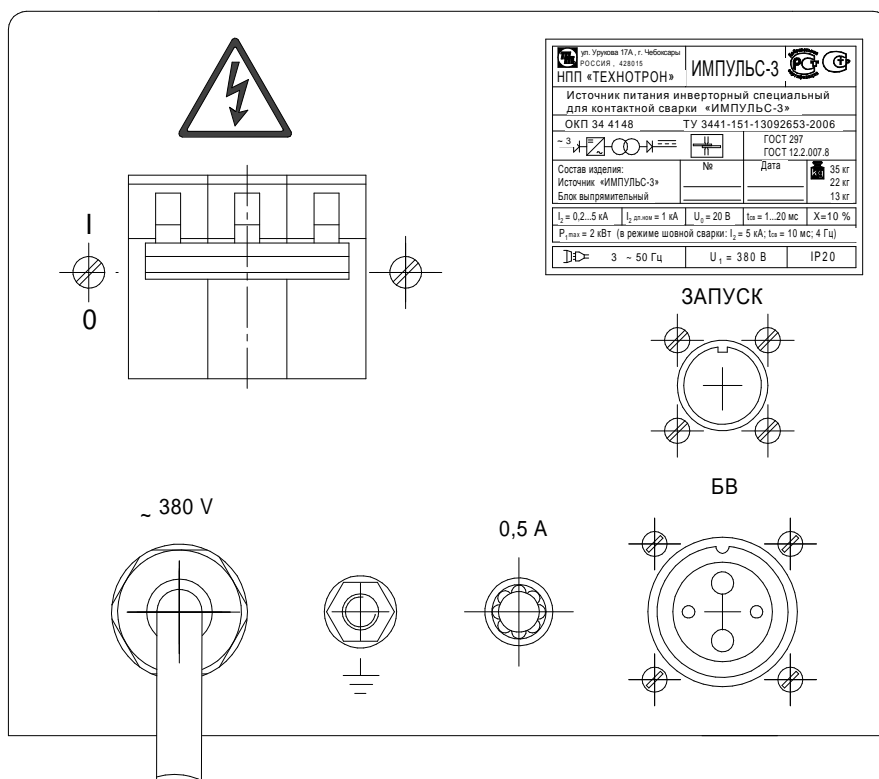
Панели источника тока контактной сварки "Импульс-3"
